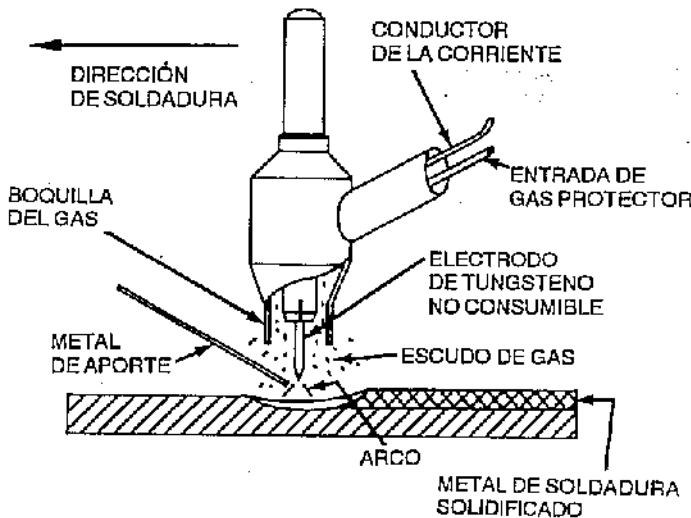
Operación de soldadura por arco de tungsteno y gas
